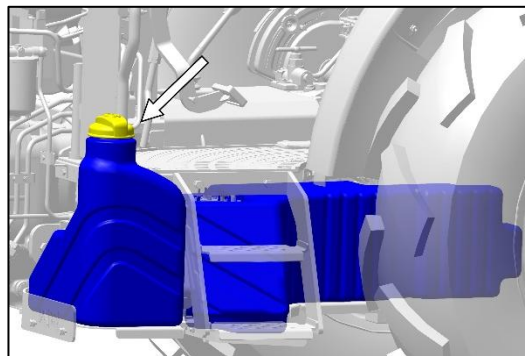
RÉSERVOIR DE CARBURANT ET BOUCHON DE REMPLISSAGE
